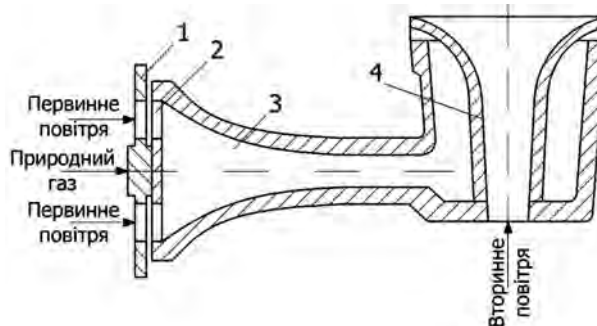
Конфорочний пальник [6]: 1 — рухома частина шибера; 2 — нерухома частина шибера, торцева поверхня пальника; 3 — змішувач; 4 — вогневий насадок.
